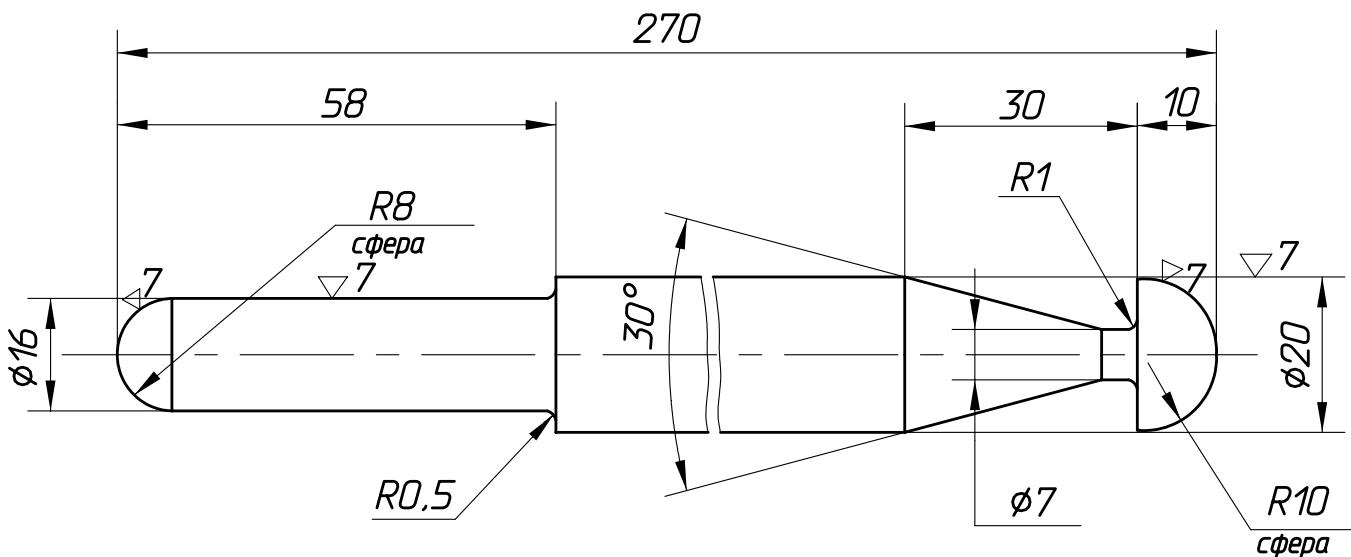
Оправка для запрессовки крышек коренных подшипников.
